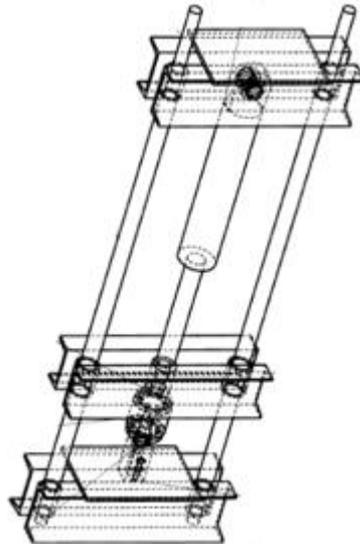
Plano 3D del antiguo banco de tracción.
